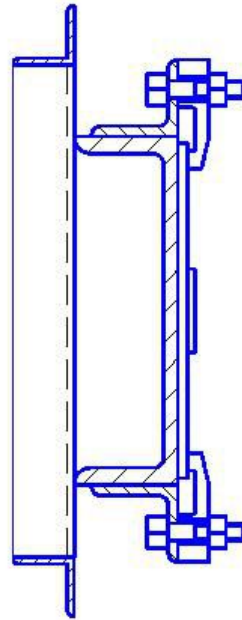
Схема крепления ножа рычажными прижимами
